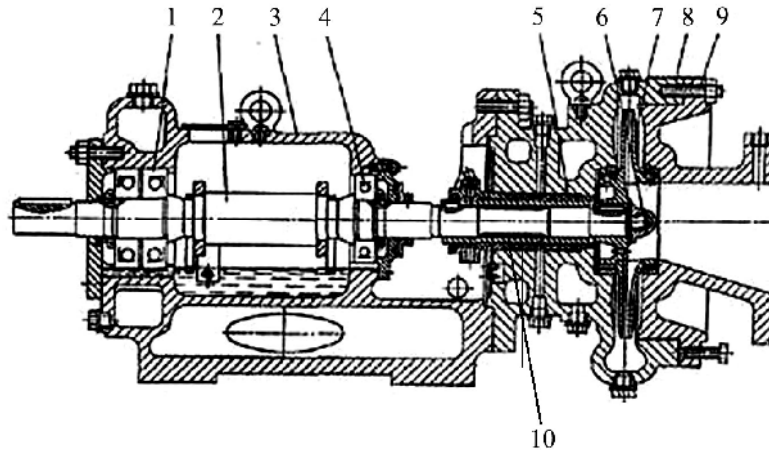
Поздовжній розріз насоса типу НКВ: 1 і 4 – підшипники; 2 – вал; 3 – опорна стійка; 5 – сальникове ущільнення; 6 – гайка робочого колеса; 7 – робоче колесо; 8 – корпус; 9 – кришка з вхідним патрубком; 10 – поверхня вала, яка зношується
